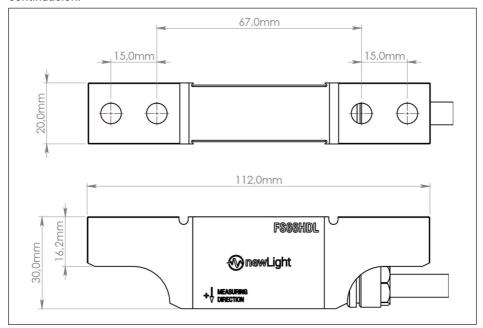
Dibujo técnico del sensor de fuerza de alta resistencia FS66HDL (dimensiones in mm)
